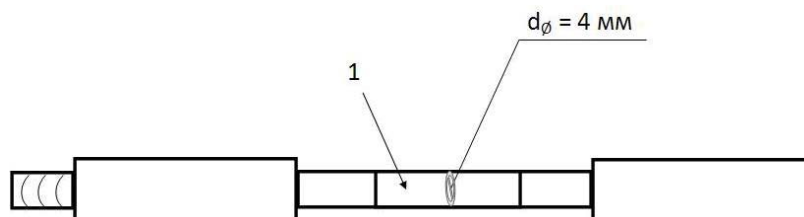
Образец сплава АМг5. Зона сварного шва (1) расположена в центральной части области локализации деформации. 1 — область сварного шва
